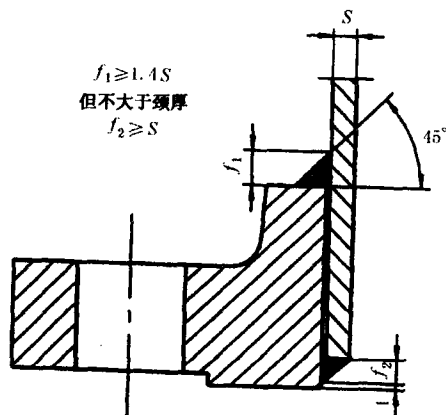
带颈平焊法兰与钢管连接的焊接接头型式
